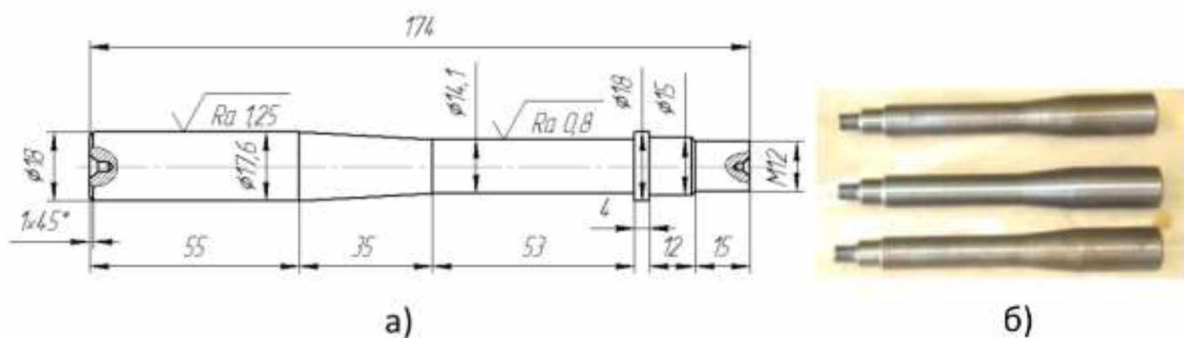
Ескіз зразка (а) і загальний вид (б) для втомних випробувань
